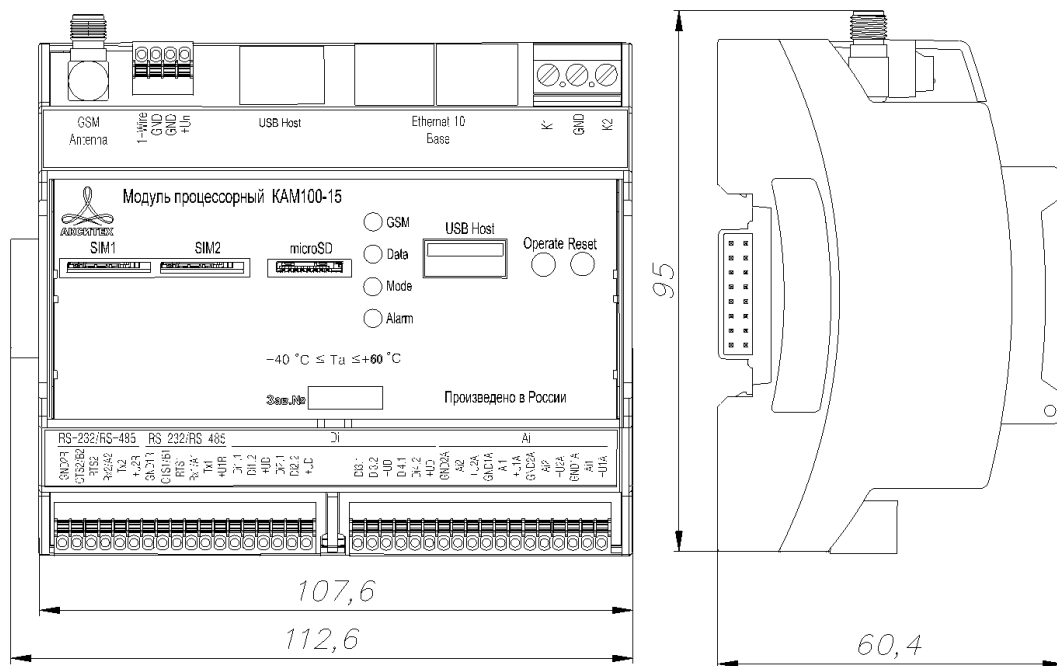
Внешний вид и габаритные размеры модуля процессорного KAM100-15
